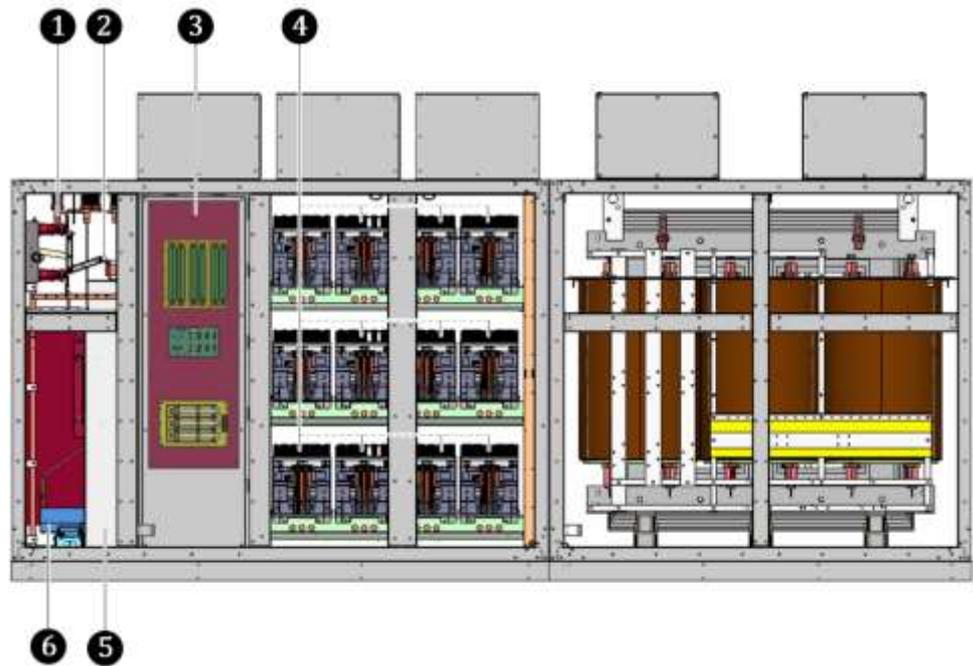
ADA-AuCom Double Access – Rückansicht
